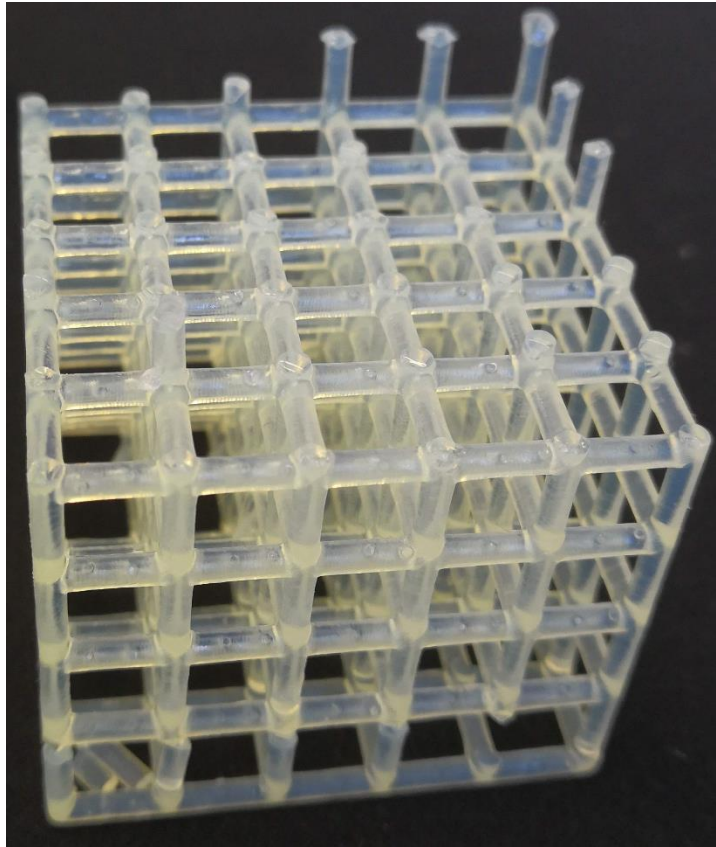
Altro esempio di struttura reticolare dopo i test di laboratorio.
